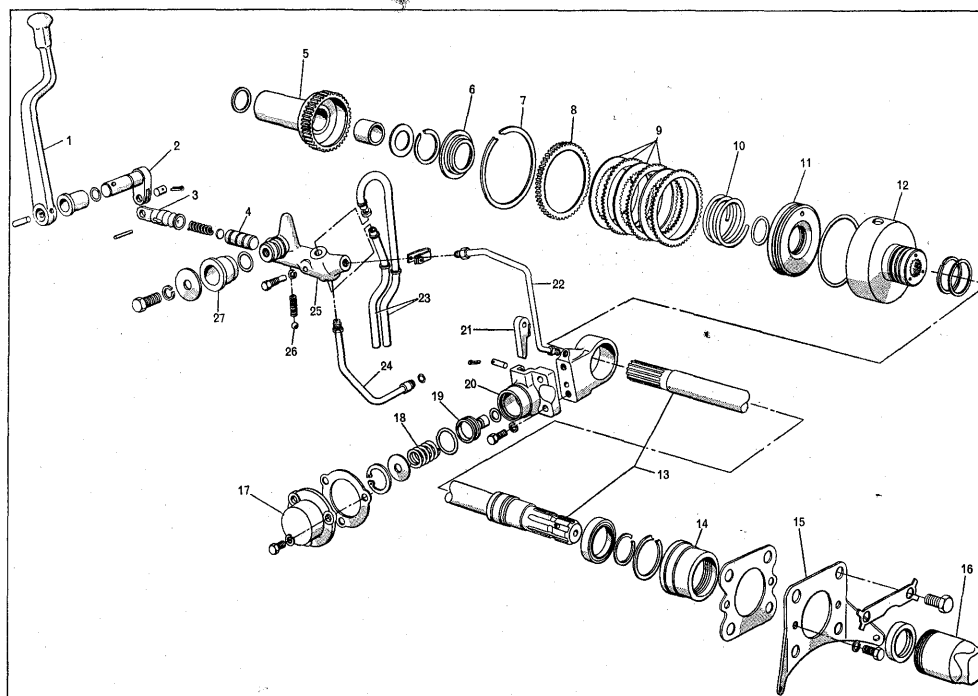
Exploded-View af det uafhængige kraftudtag.
